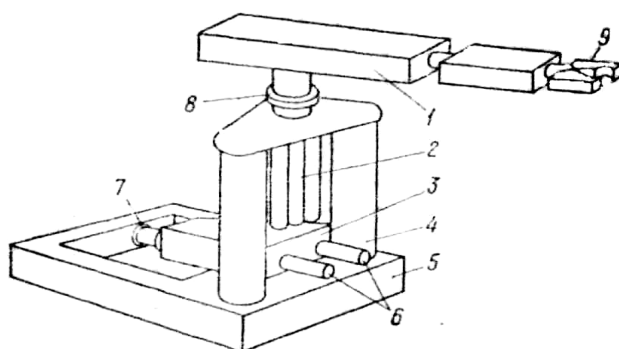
Напольный робот с выдвижным манипулятором и консольным механизмом подъема
